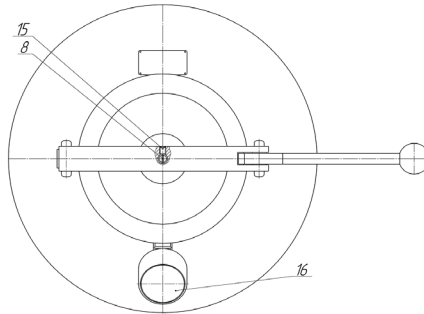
Загальний вигляд пристрою ПГС-2 (вид зверху)
